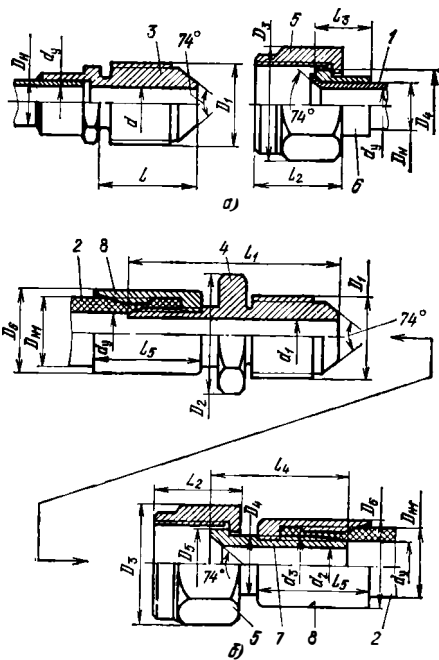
Разъемное штуцерное соединение: а — для металлических труб; б — для гибких рукавов; 1 — труба металлическая; 2 — рукав резиноканевый; 3 — штуцер; 4 — штуцер для рукава; 5 — гайка накидная; 6 — ниппель; 7 — ниппель для рукава; 8 — муфта для рукава
